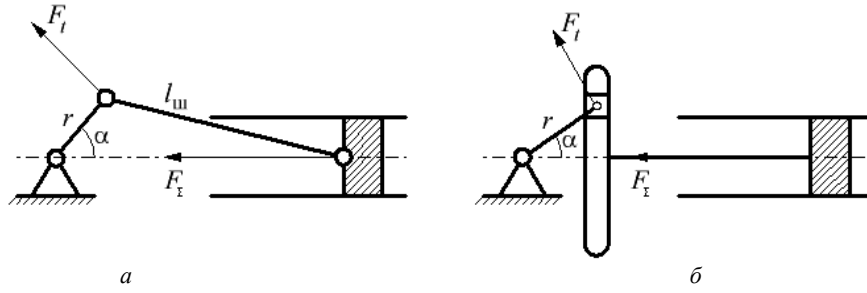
Идеализованная кинематическая схема кривошипного механизма компрессора:
